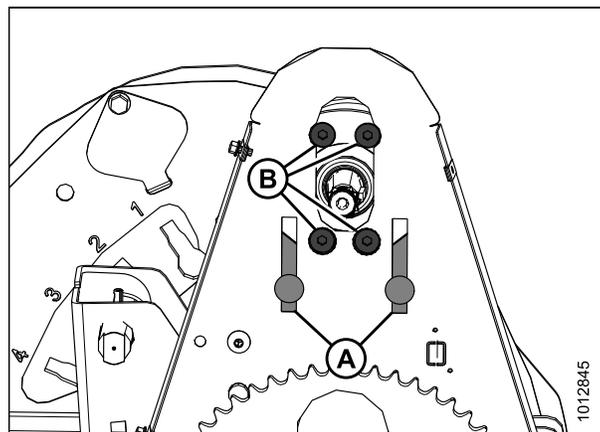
Монтажные отверстия мотора привода подбирающего мотовила
